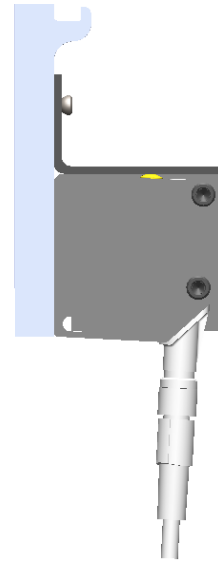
Vista lateral. Diseño del montaje de sensor y tope.
